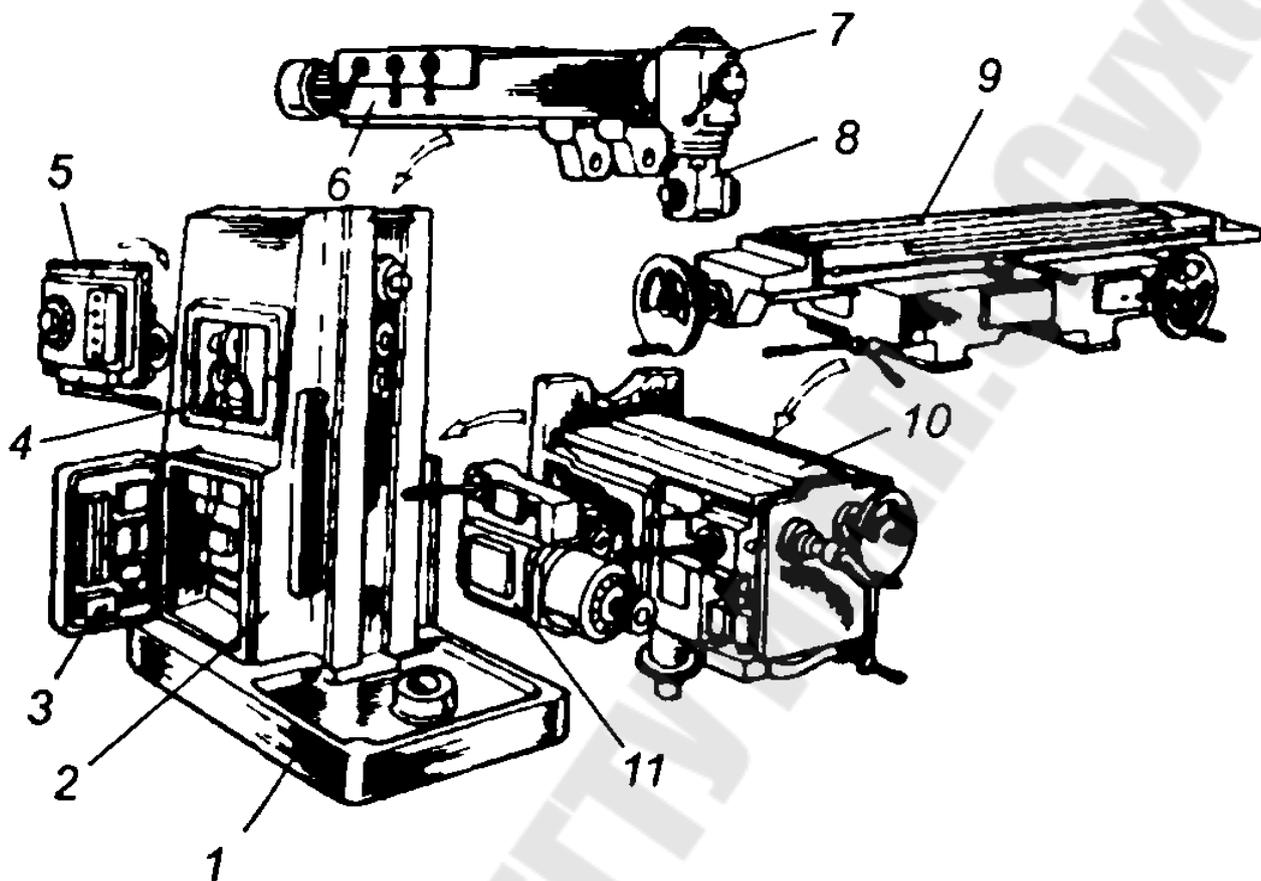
Основные узлы широкоуниверсального консольного фрезерного станка
